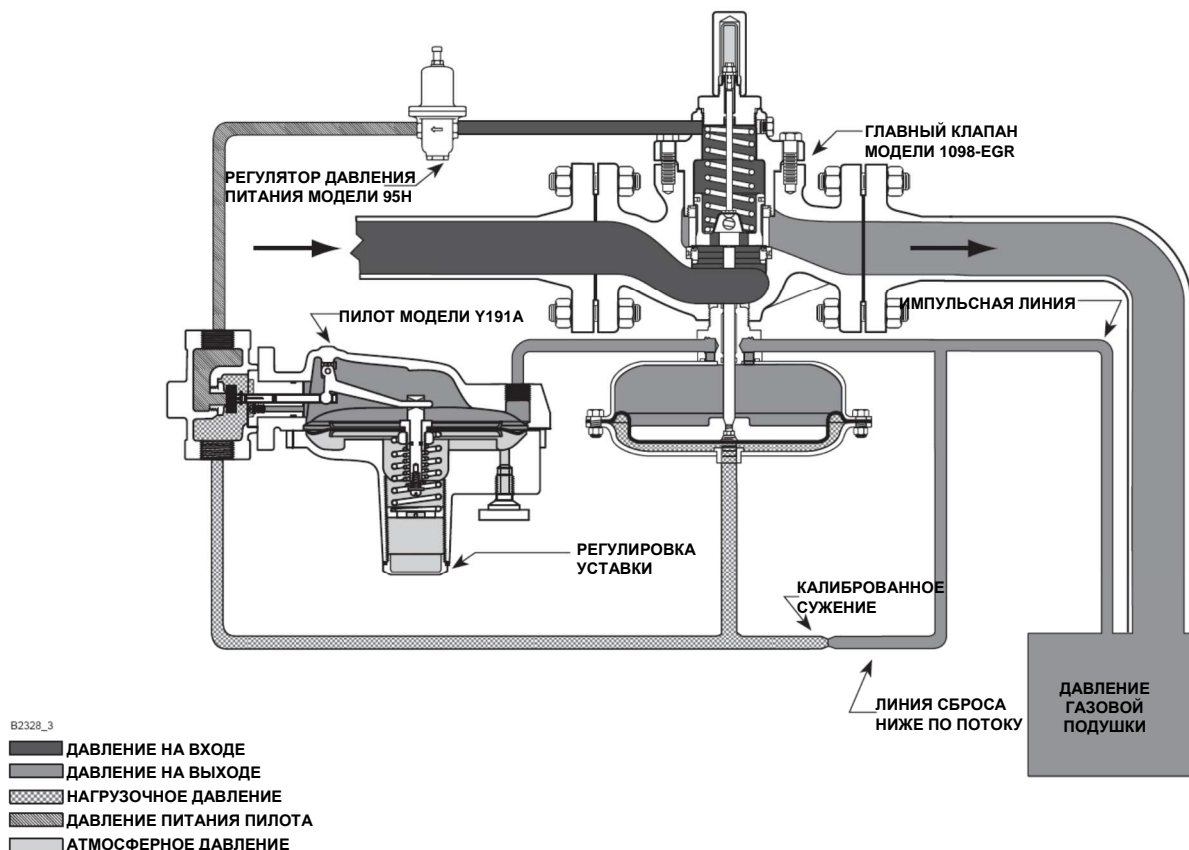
Схема работы регулятора НД газовой подушки типа 1190
